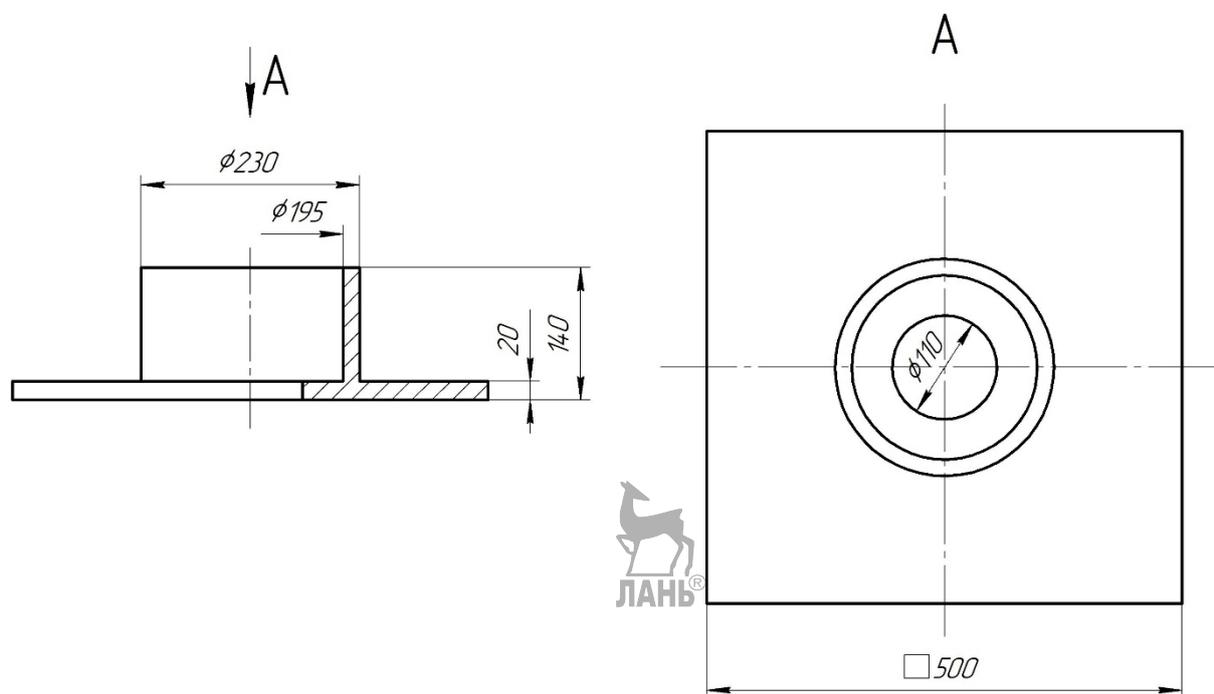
Чертеж нижней пластины корпуса ОПУ
